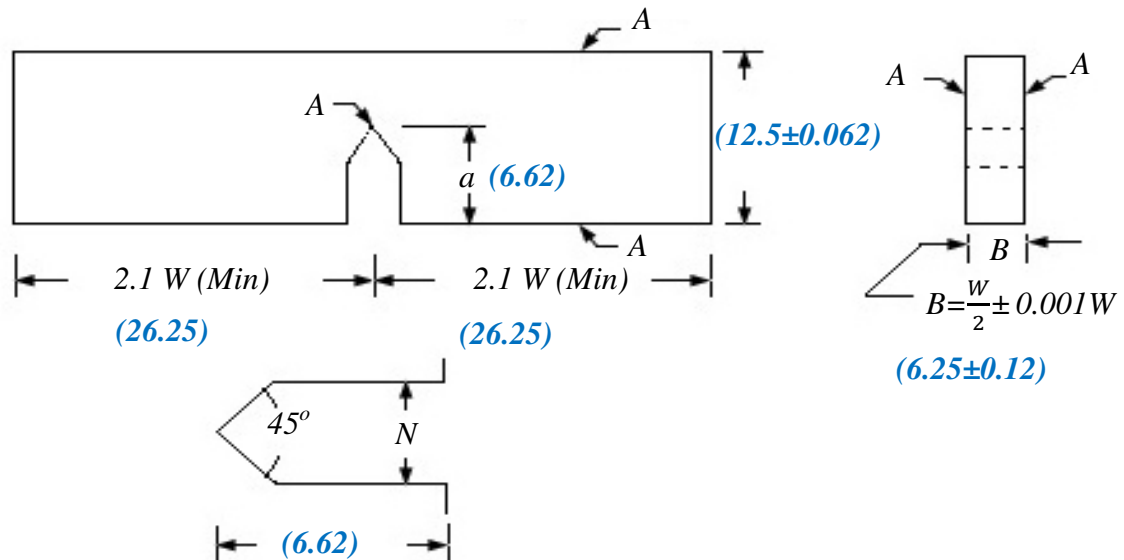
Dimensiones de probetas para ensayo de tres puntos (mm)
